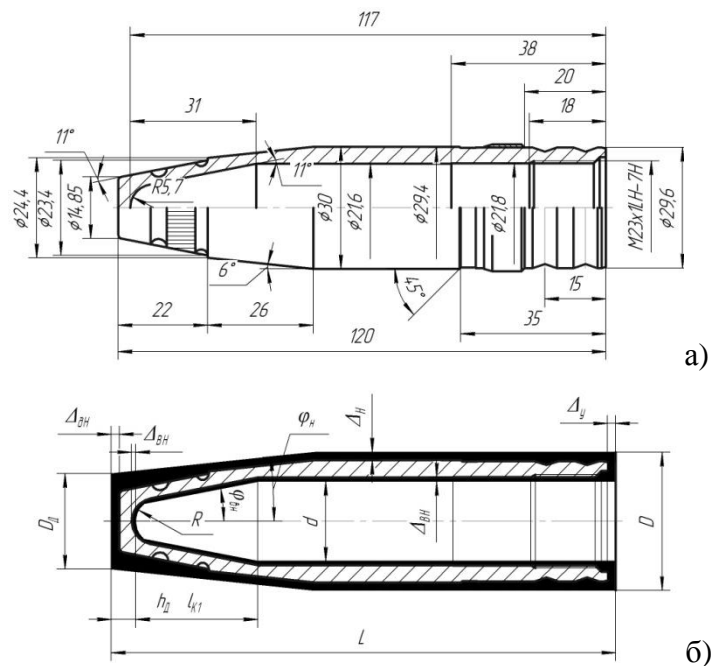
Размеры готовой детали (а) и заготовки с припусками на механическую обработку (б)
